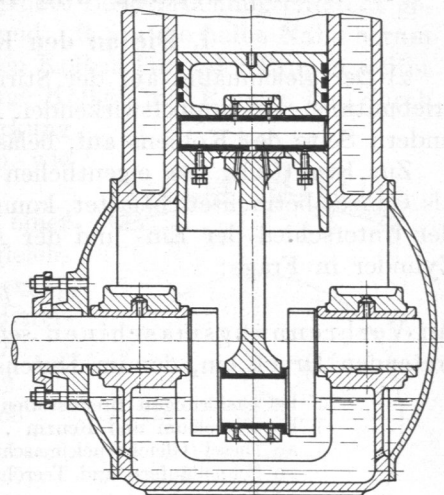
Schmierung durch Ölbad an einem Kompressor der Deutschen Maschinenfabrik A.-G., Duisburg.
